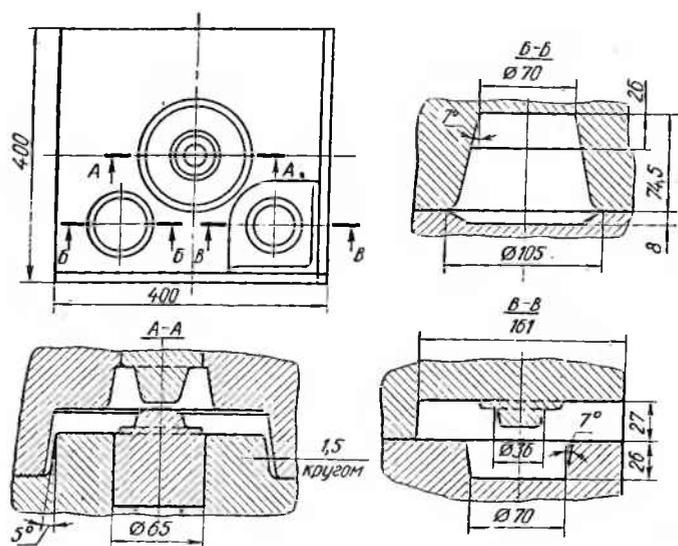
Молотовый штамп для закрытой штамповки поковки зубчатого колеса в три перехода
